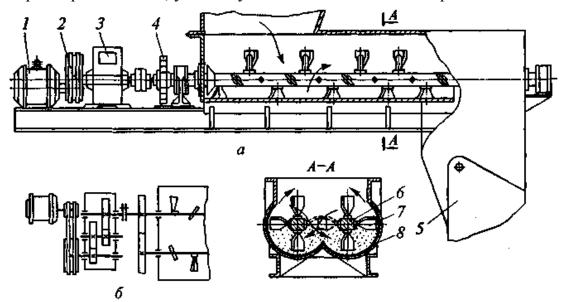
Горизонтальный двухвальный смеситель непрерывного действия (a) и кинематическая схема его привода (б)
